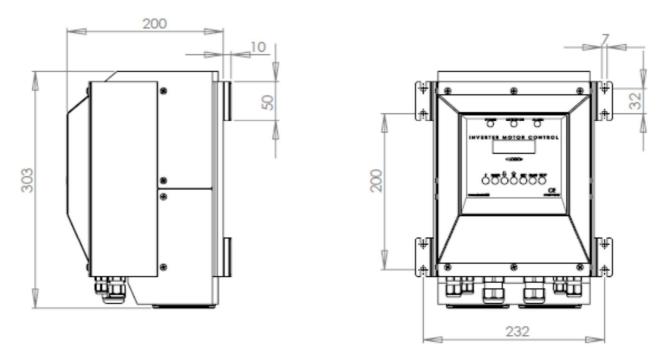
Dimensioni e quote di fissaggio a parete for ITTP(D) 4.0-5.5-7.5 W
